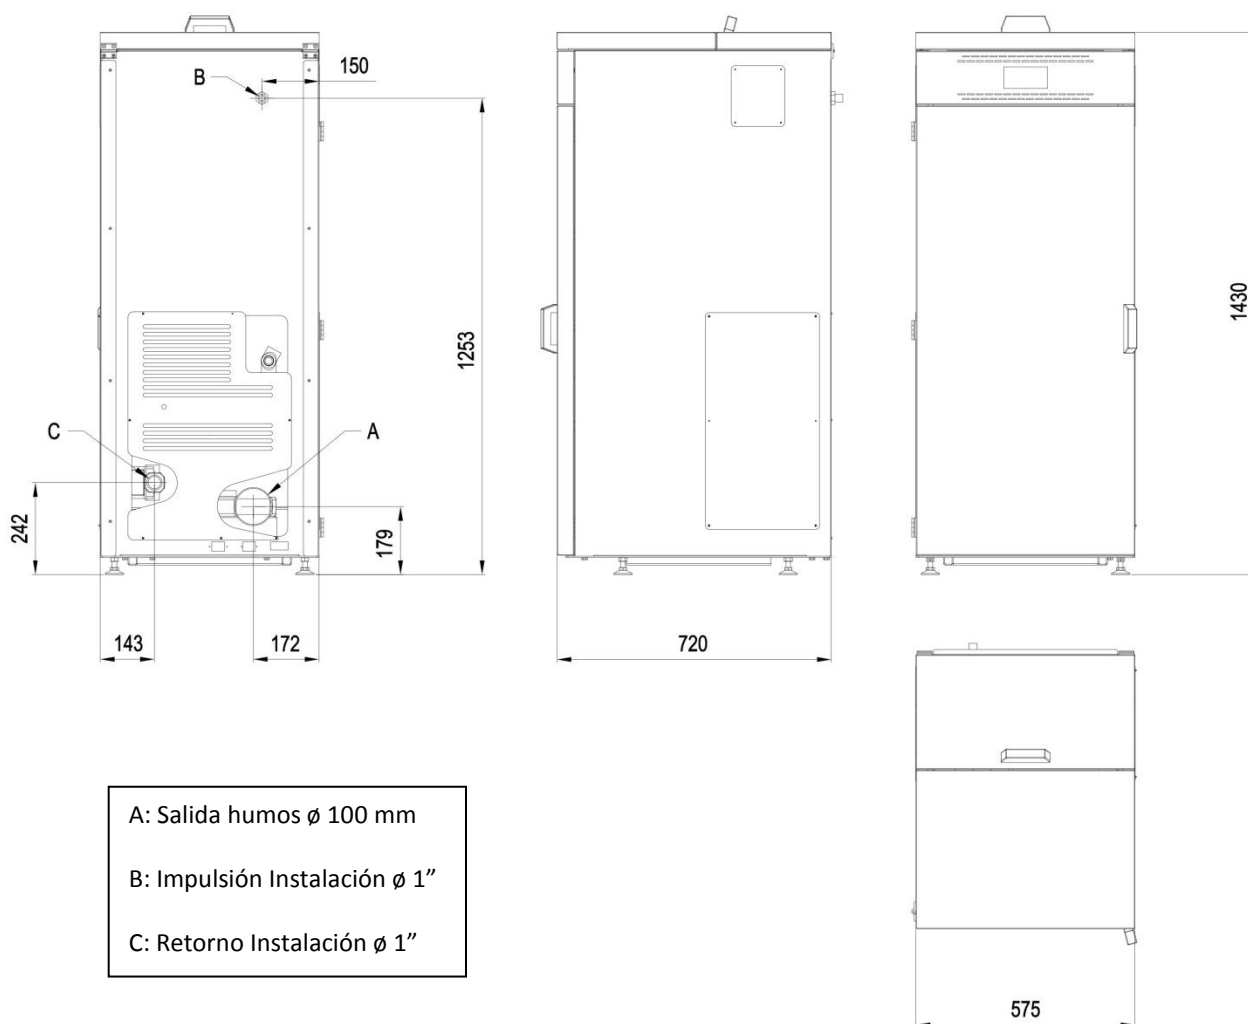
DIMENSIONES DE LA CALDERA DE PELLET SINTESI en mm.
